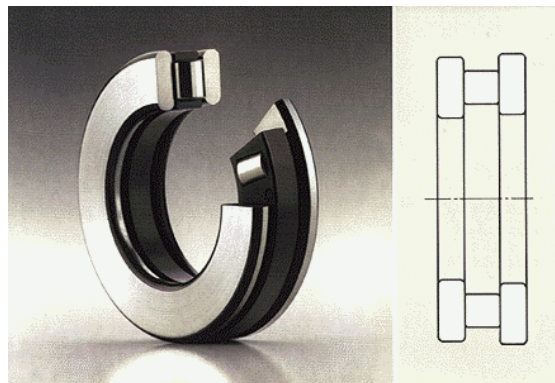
Rodamiento axial de rodillos cilíndricos.
